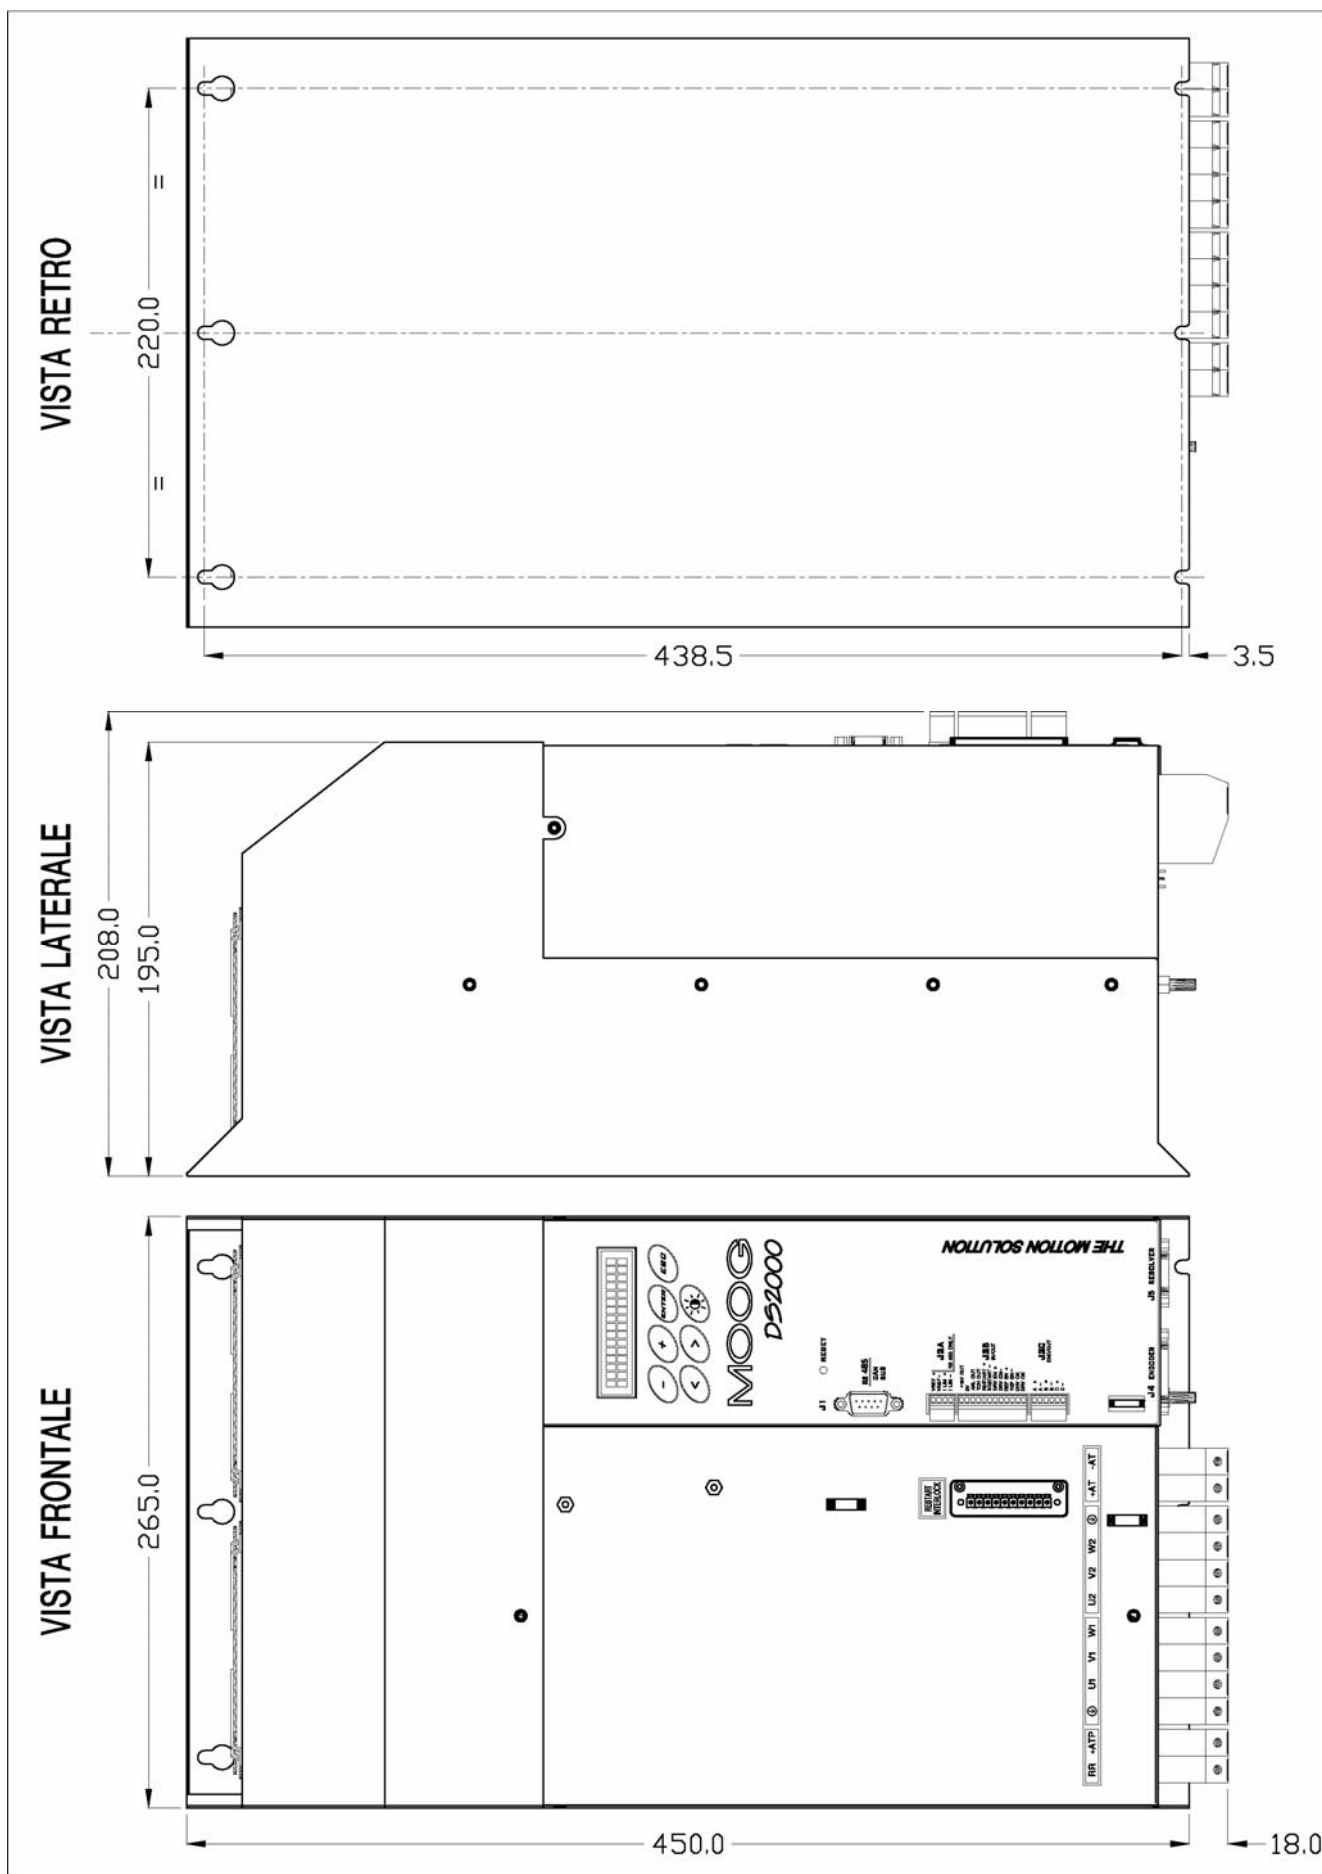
Dimensioni e fissaggi (mm) taglia D
